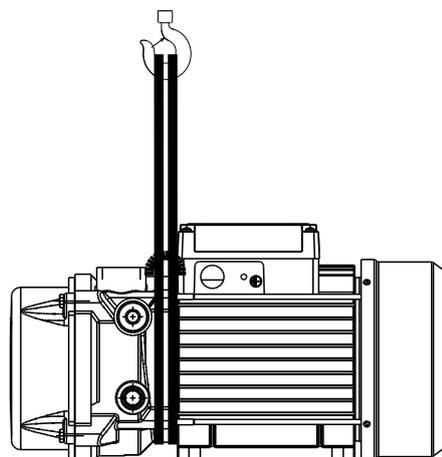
Hebezeuge befestigen an Pumpenaggregat
